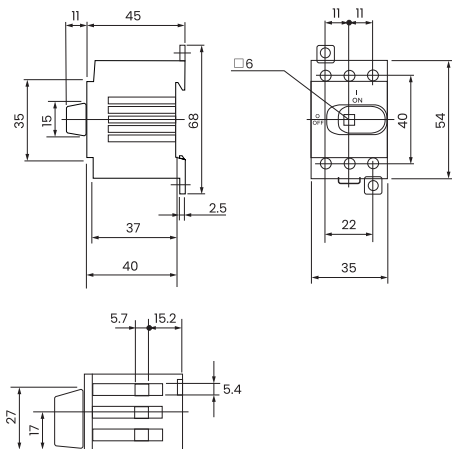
Габаритные и установочные размеры рубильников 40А 3Р
